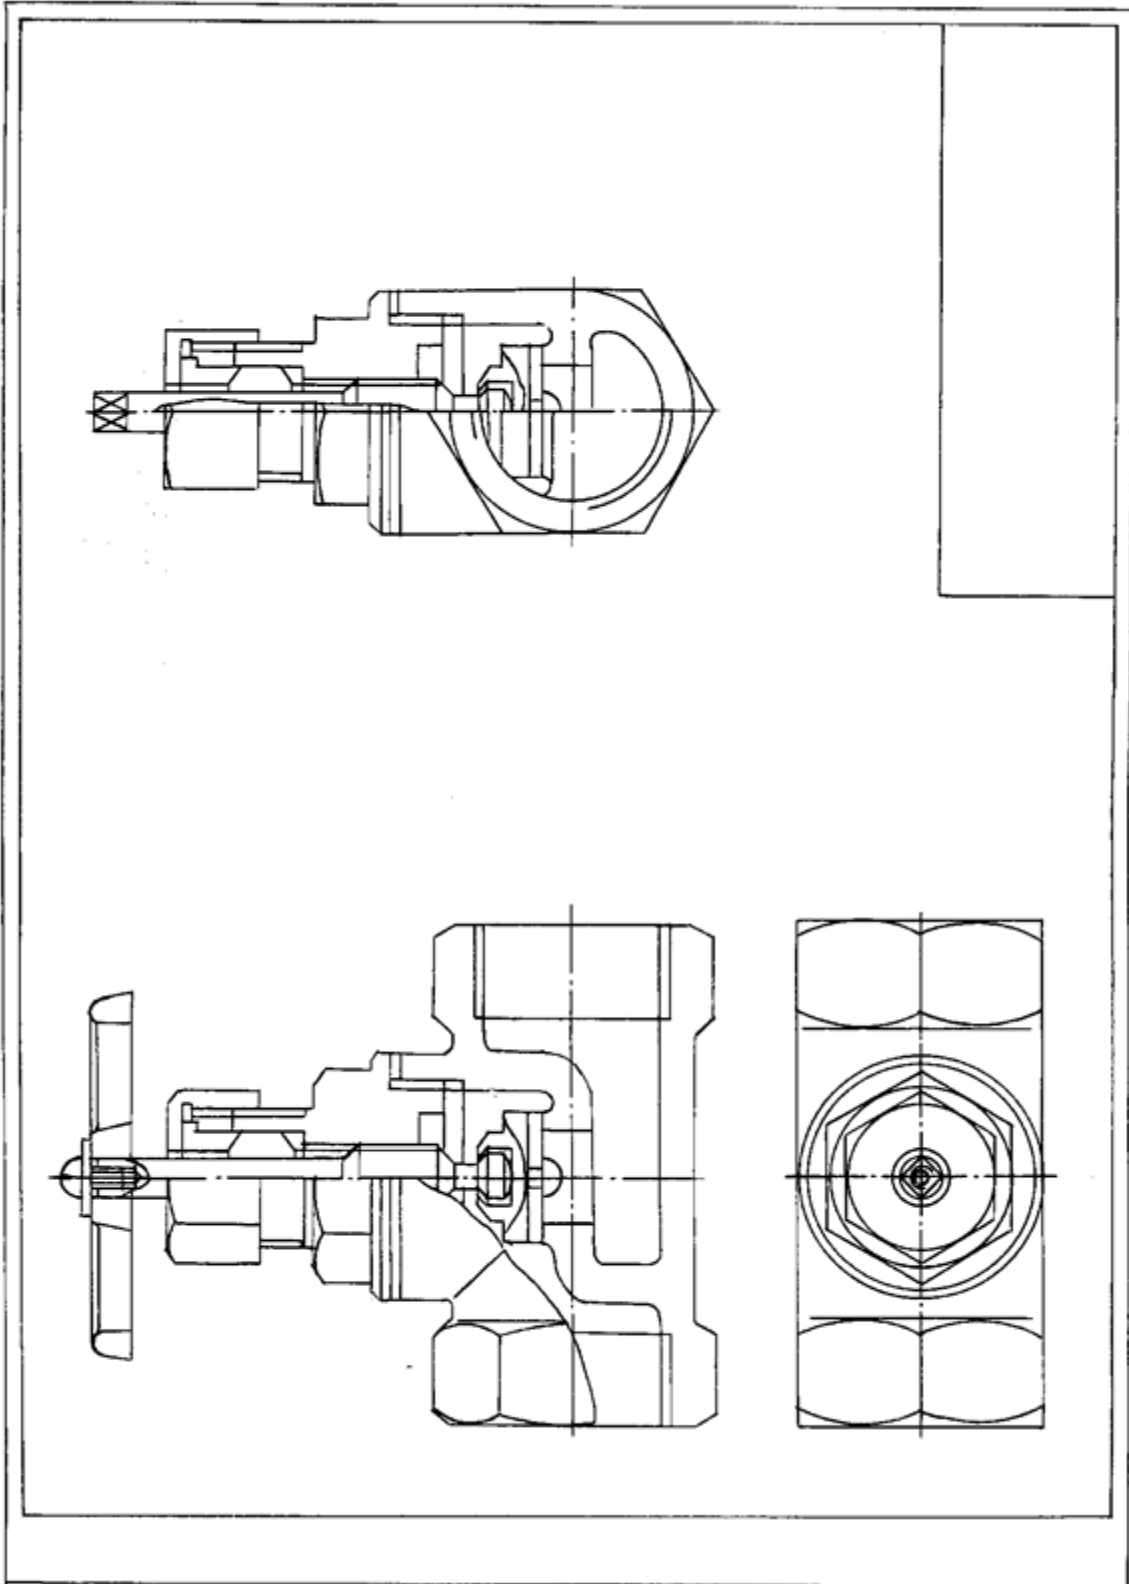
Эскиз сборочного чертежа «Вентиль»
